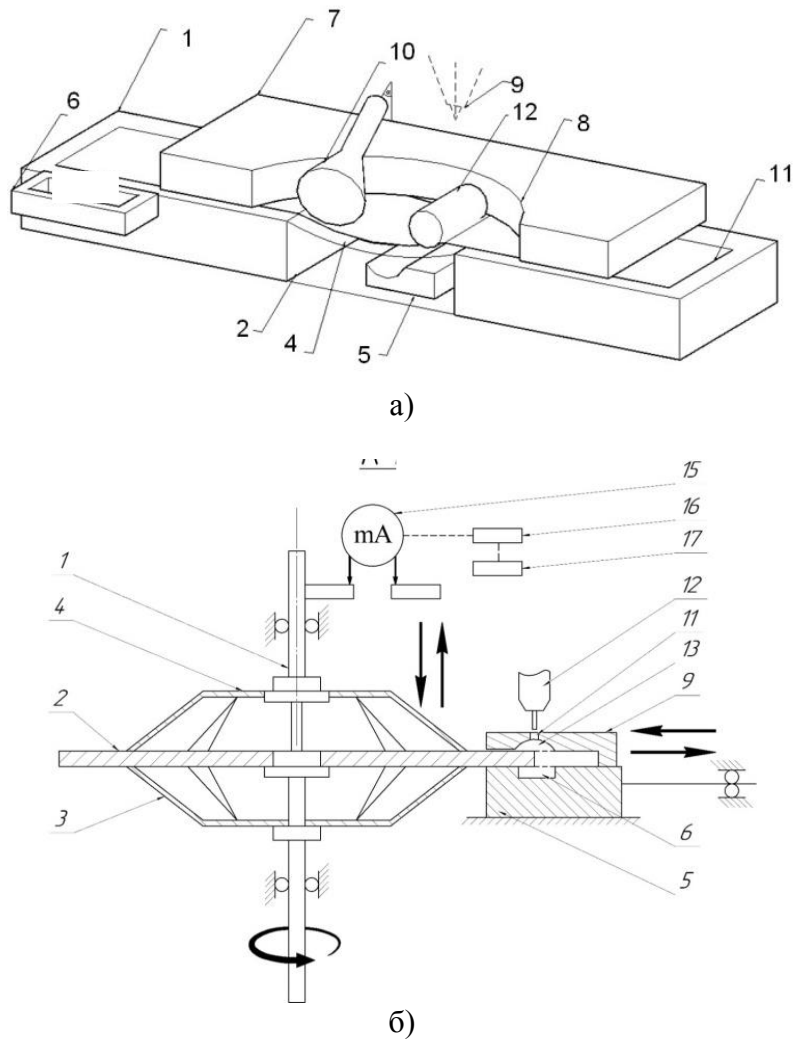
Схеми пристроїв для наплавлення тонкостінних деталей: а) пласкої форми; б) дискової форми
